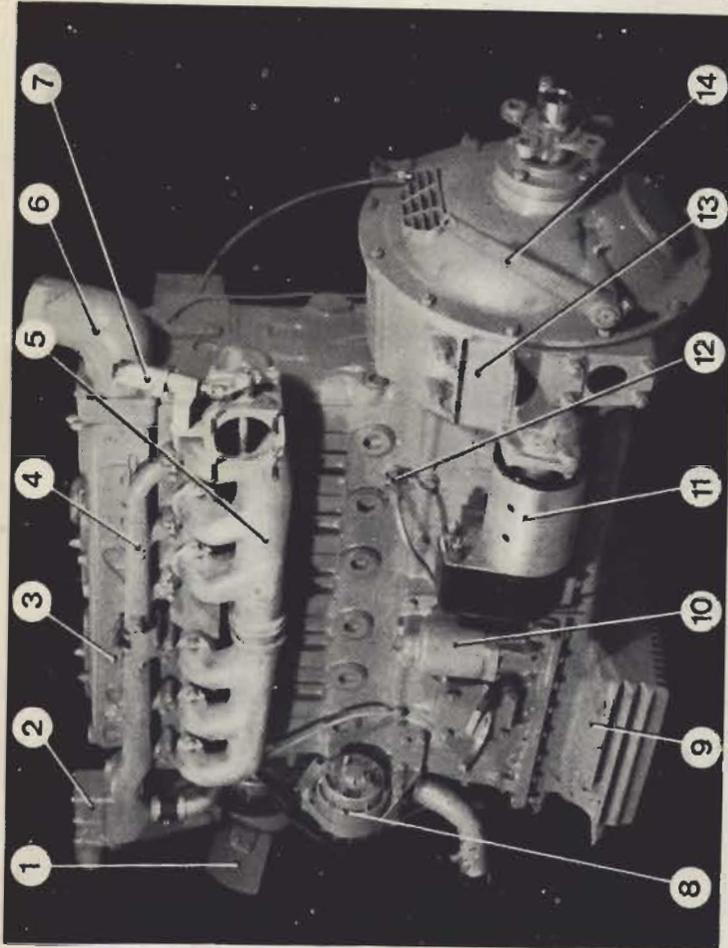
Motor 9105/15 (lado izquierdo)
